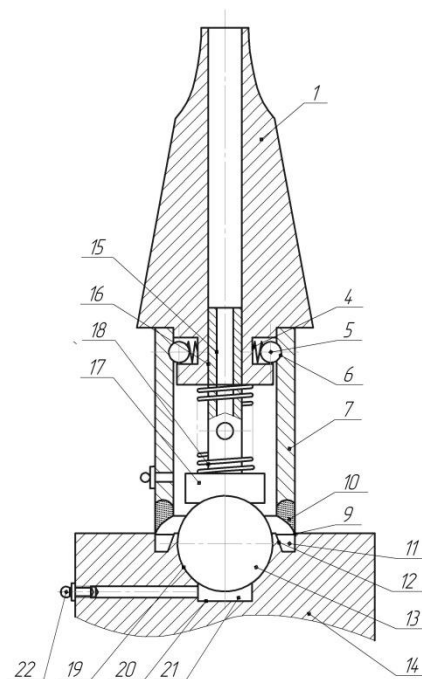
Пристрій для завальцювання кульок в корпусних деталях
